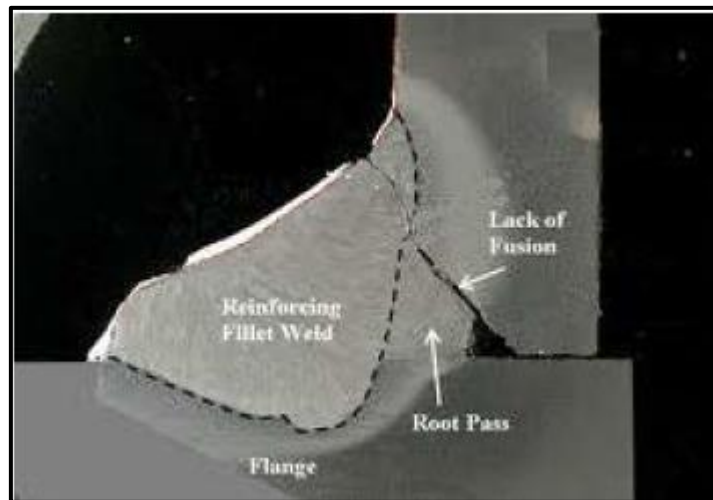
Manque de fusion à la racine de la soudure.
